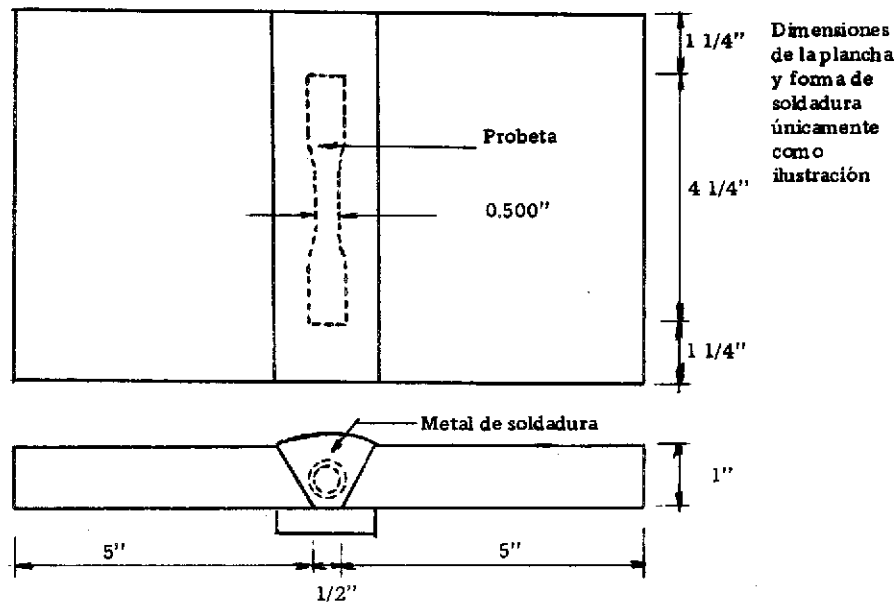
Plancha de prueba para extraer espécimen para ensayo a tensión del metal de soldadura
